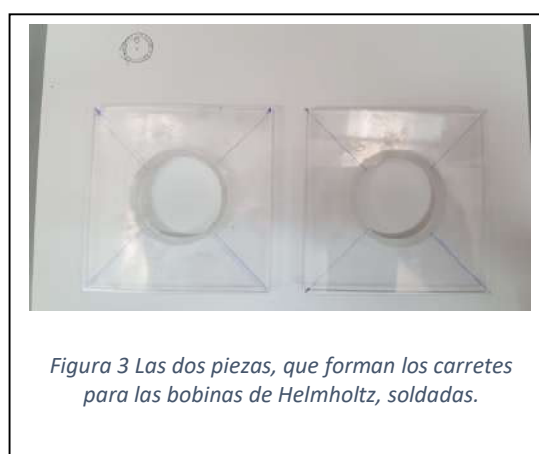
Las dos piezas, que forman los carretes para las bobinas de Helmholtz, soldadas.
